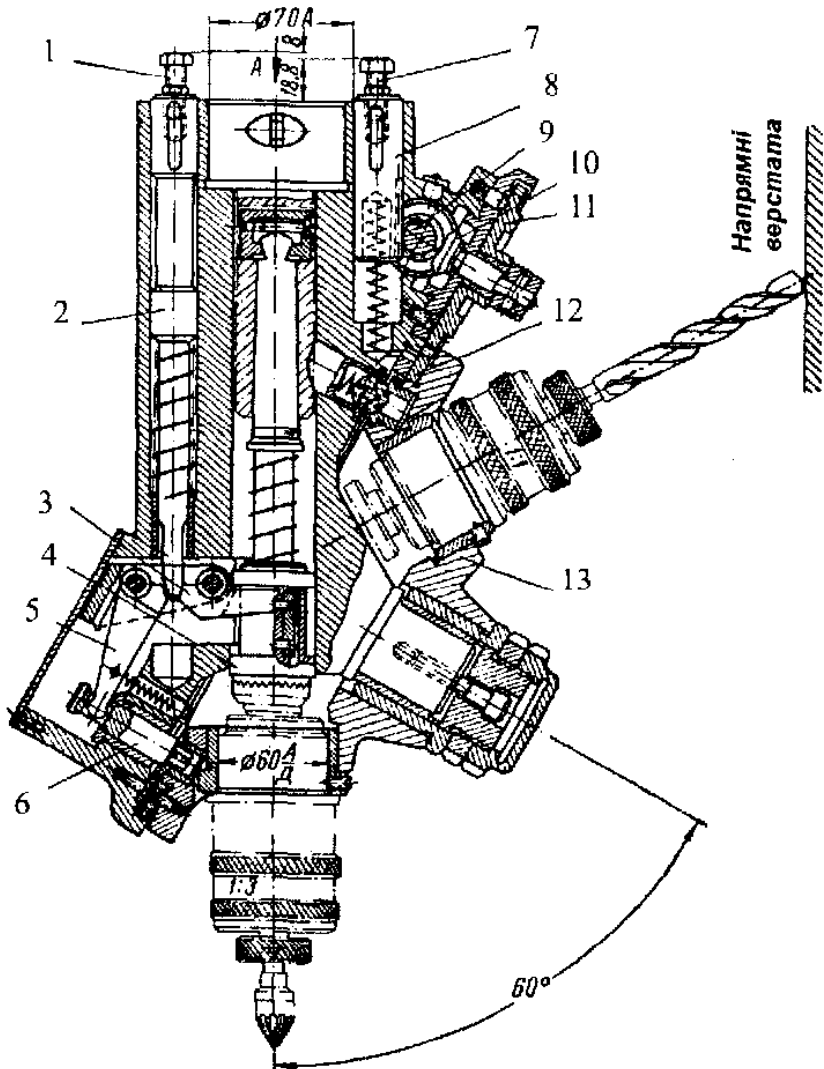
Револьверна головка з автоматичним поворотом
